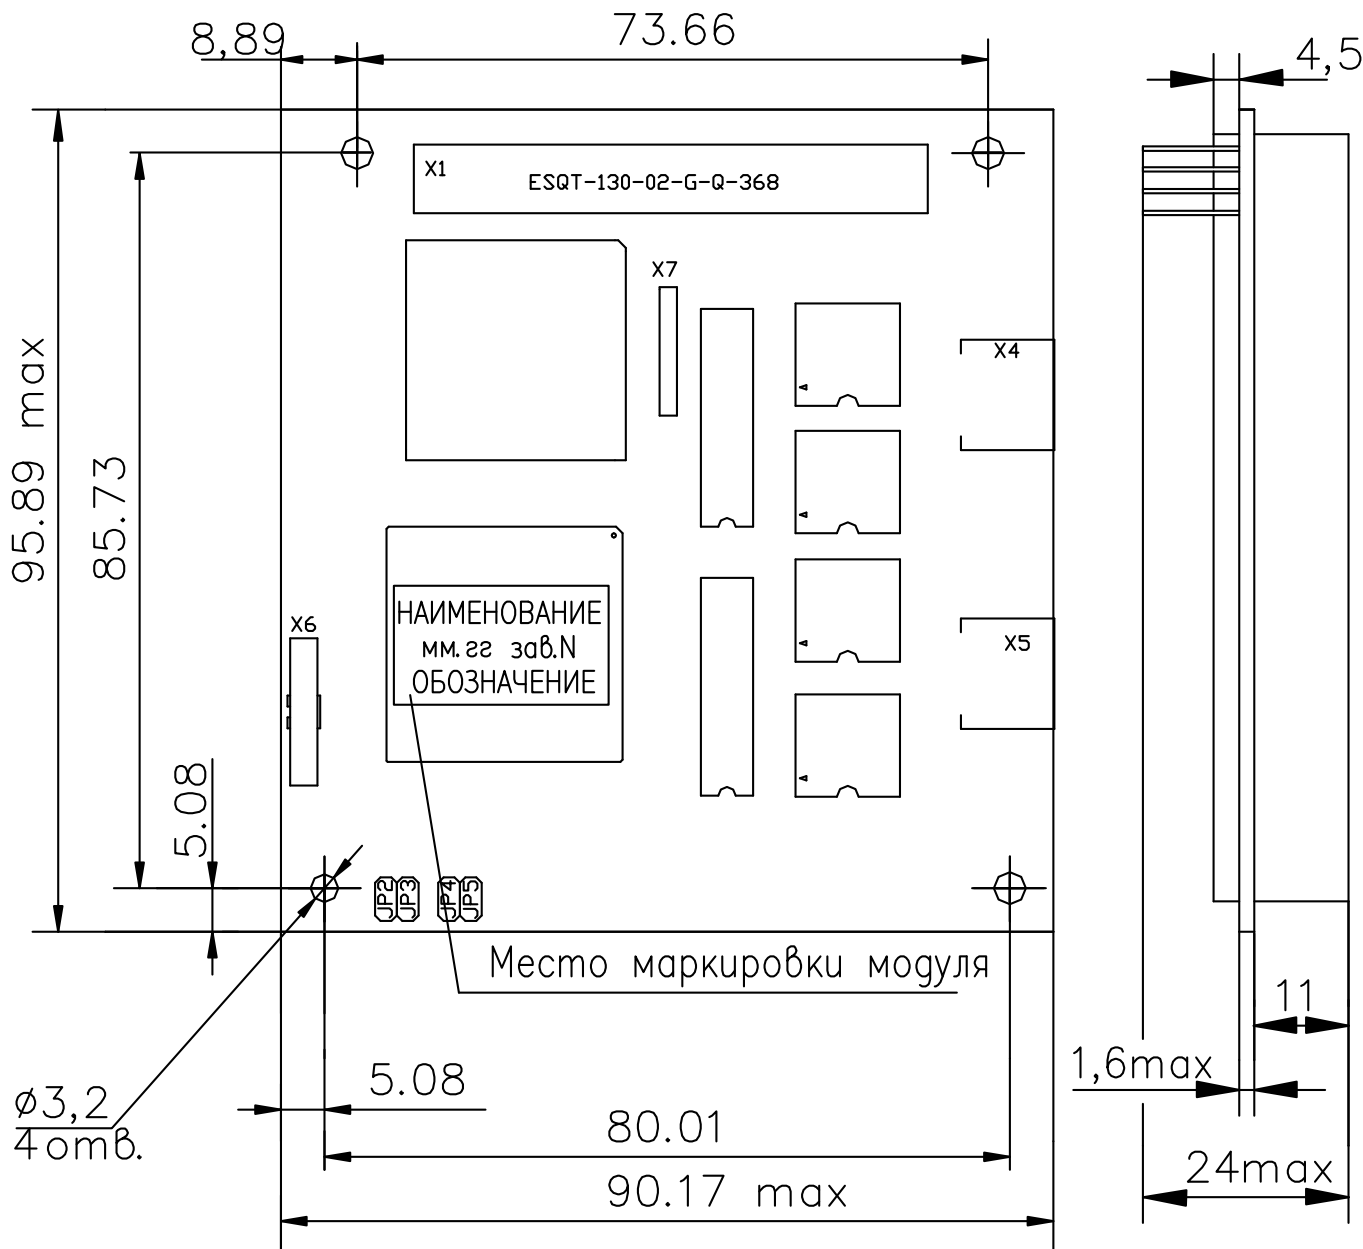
Габаритный чертеж изделия с двумя резервированными каналами без разъемов X2, X3
